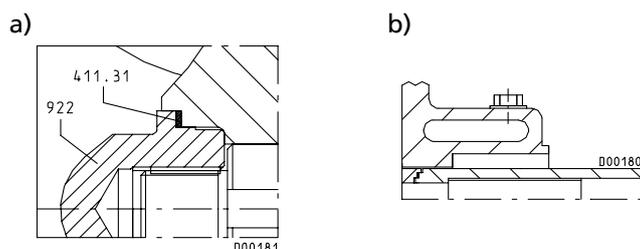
а) крепление рабочего колеса, подшипниковый кронштейн P08s и б) активно охлаждаемая камера уплотнения вала
